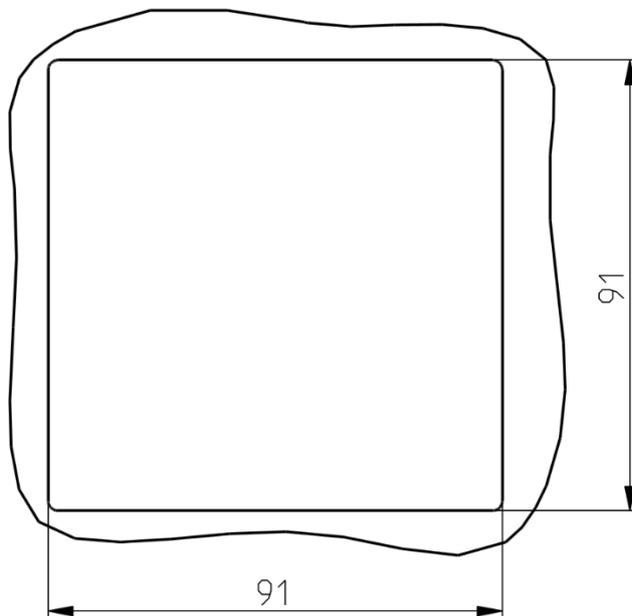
Maßzeichnung Schalttafel Ausschnitt
